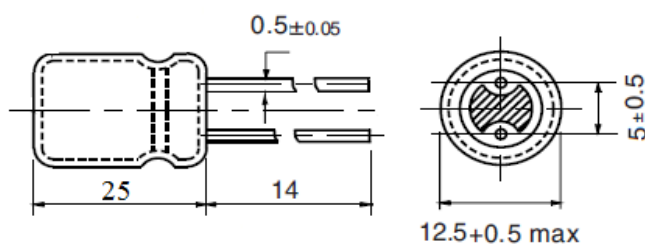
Конструкція конденсатора FRA-25 В-1800
